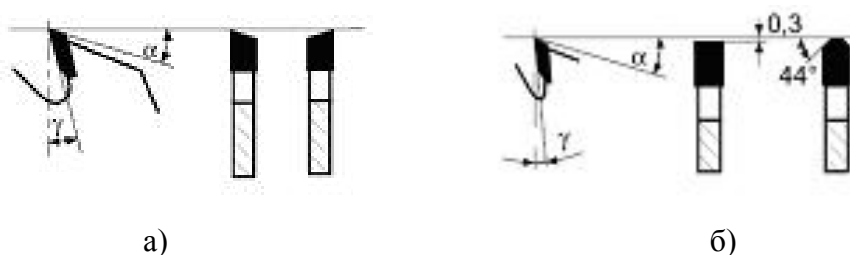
Профили зубьев дисковых пил с пластинами твердого сплава для распиловки ламинированных ДСтП: а – попеременно косой; б – плоско-трапецевидный
